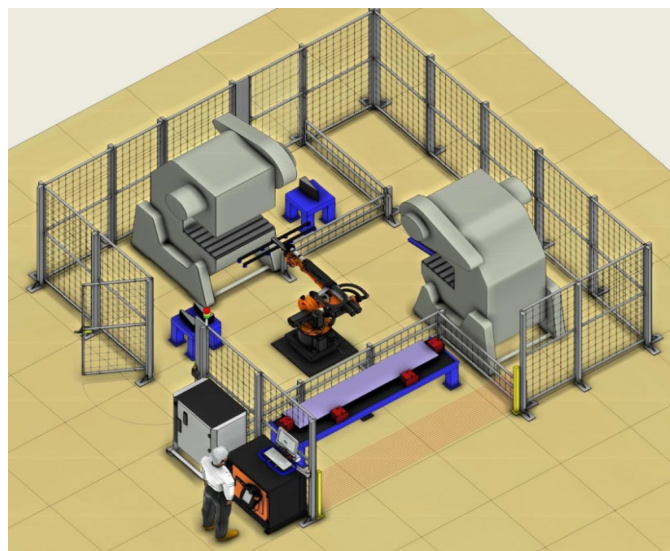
Роботизированный технологический комплекс изготовления деталей типа «нервиюры»
